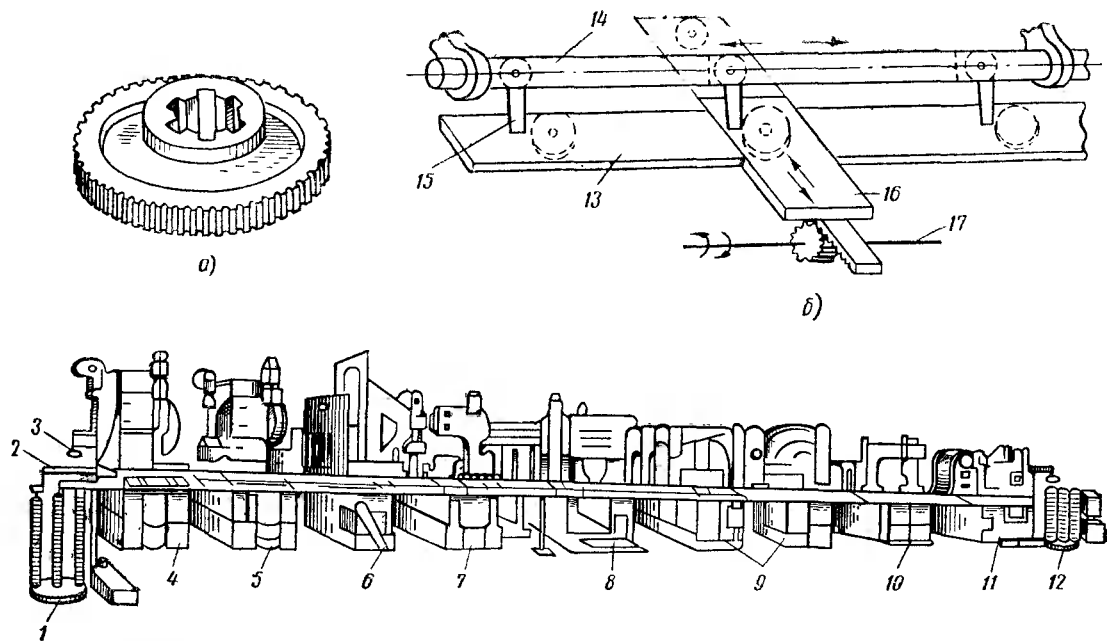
Автоматическая линия для обработки зубчатых колес:
